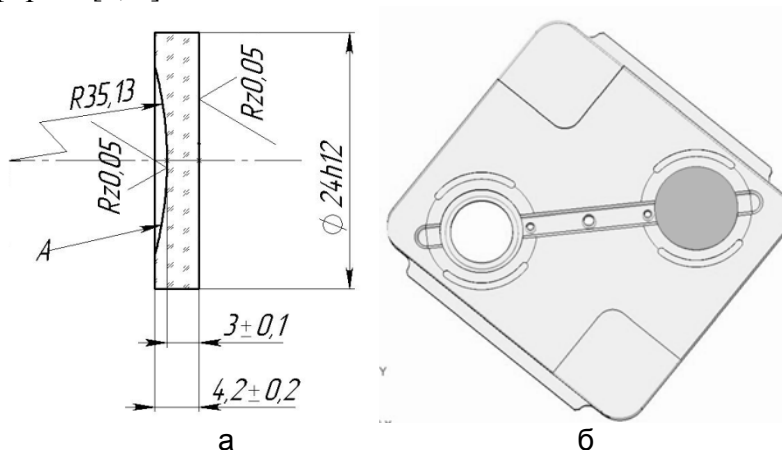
Чертеж исследуемой линзы (а) и модель формообразующей детали для линзы (б)
